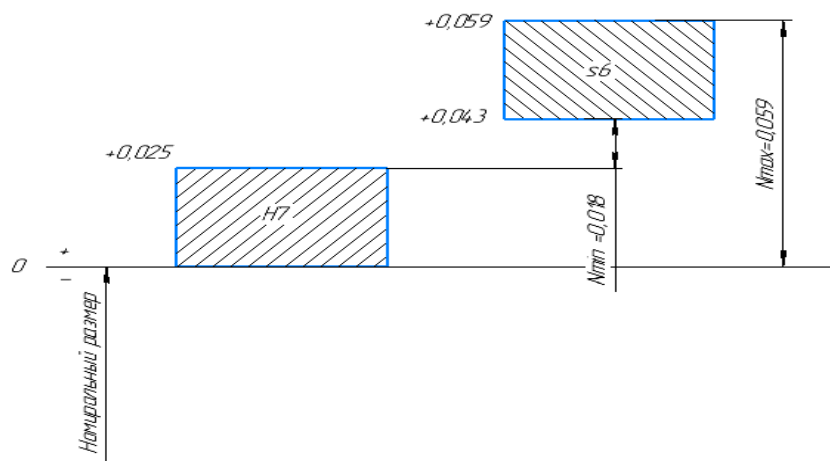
Схема расположения полей допусков посадки с натягом
